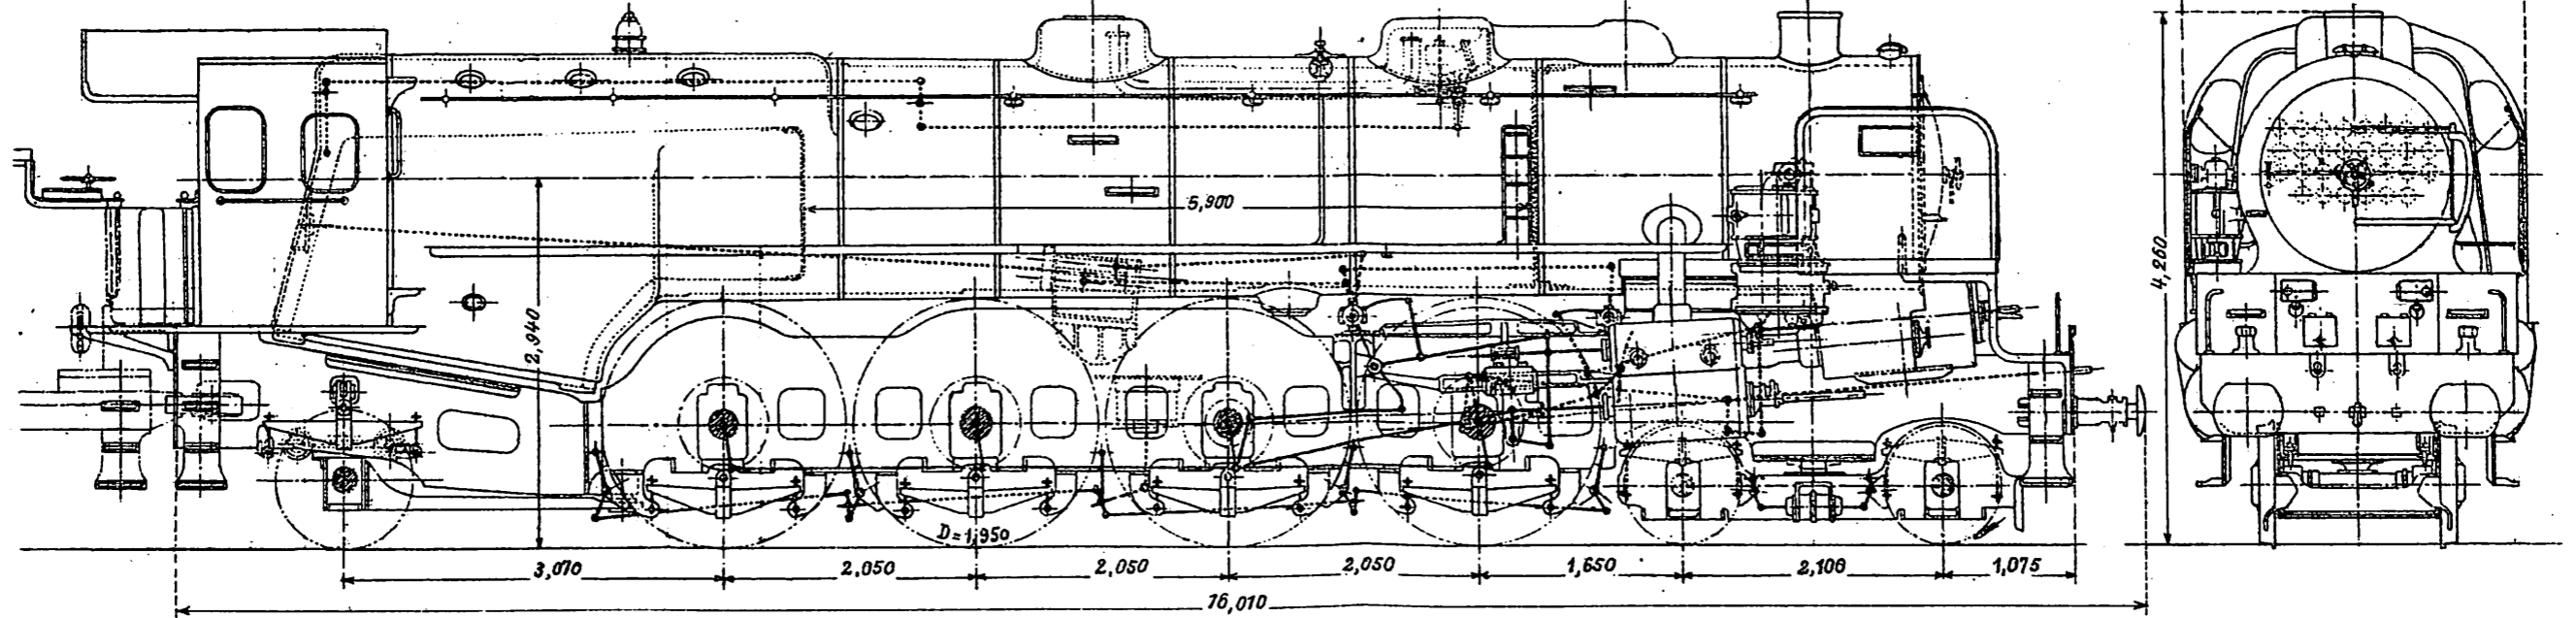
2 D 1 Vierzylinder-Verbund-Schnellzuglokomotive mit 4 gekuppelten Achsen der P. L. M. Bahn. Maßstab 1 : 60.
